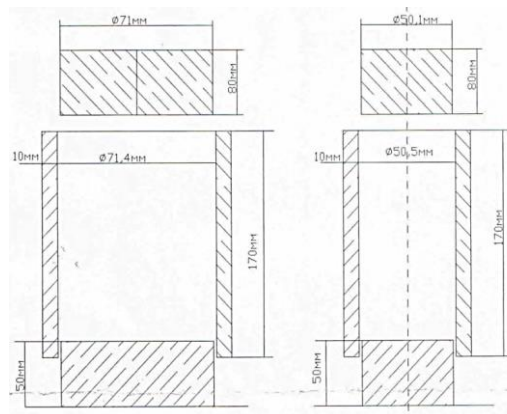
Формы для изготовления мелкозернистых и песчаных образцов
